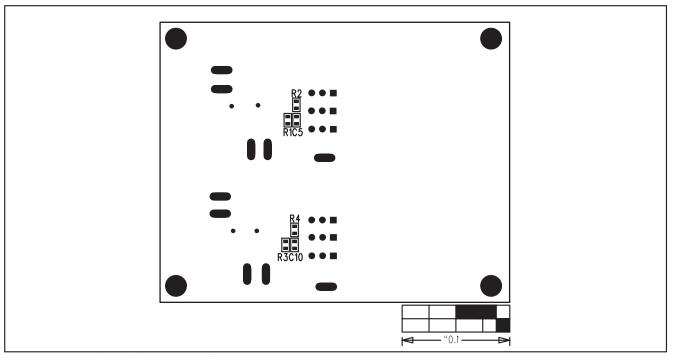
MAX1556 评估板元件布局图 — 焊接面
